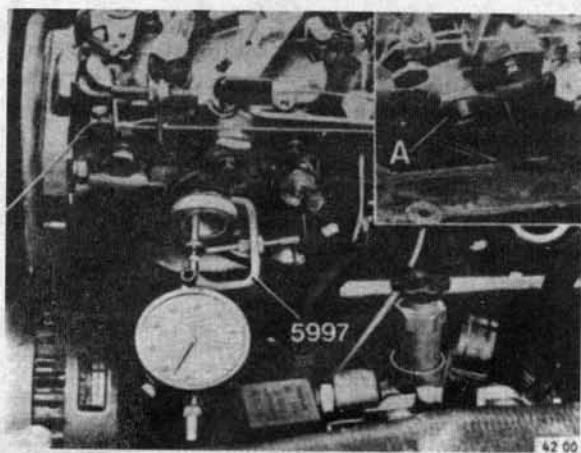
Установка коленвала при регулировке ТНВД
